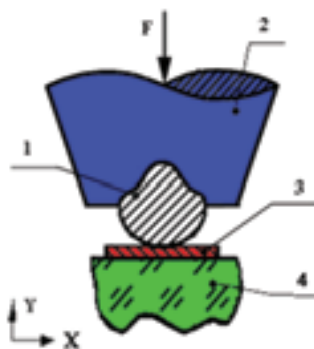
Схема УЗ сварки: 1– проволока; 2– сварочный инструмент; 3 –контактная площадка; 4 – кристалл
